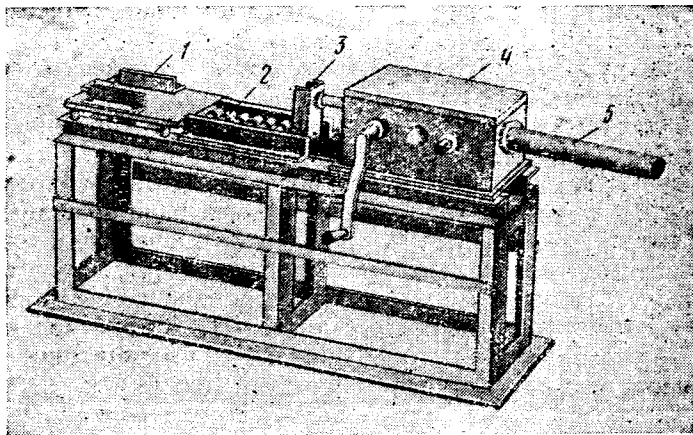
Приспособление для запрессовки блока пластин в сосуд:
